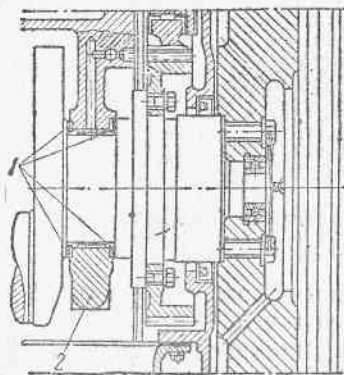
Задняя опора коленчатого вала двигателя ЯАЗ-204.
